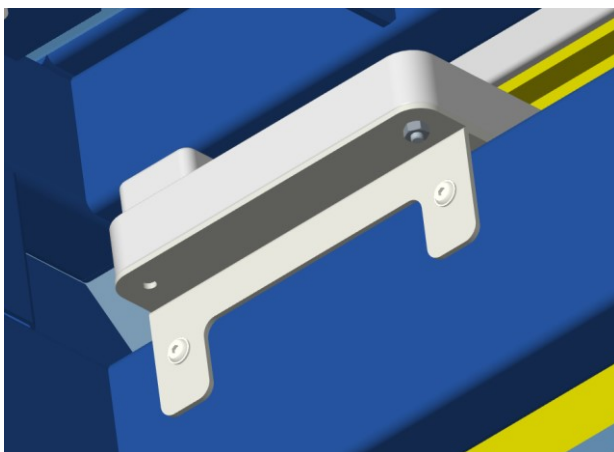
Zjednodušený model kontroléru motoru a jeho umístění
